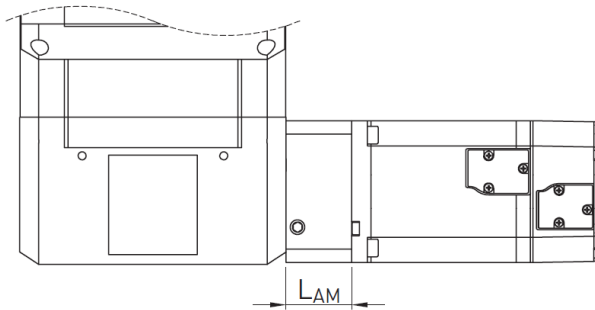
Motoranbindung Linearmodul HM-B ohne Getriebe
